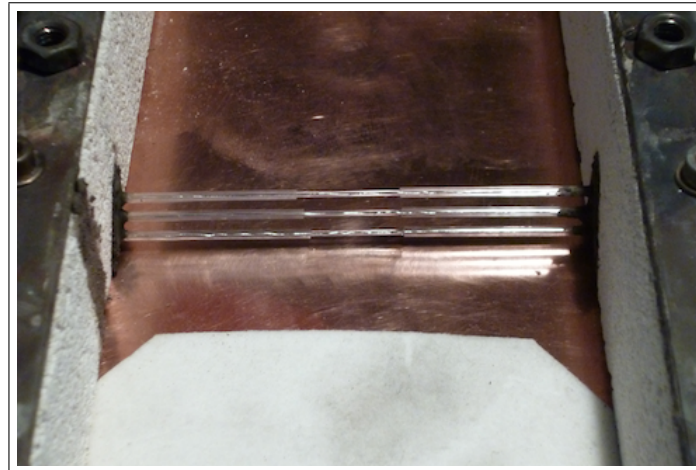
Eingemauerte Tauchelementmessung mit Blick in Gießrichtung (unterer Bildrand: Wärmedämmung mittels Aluminiumsilikatfasermatte)
